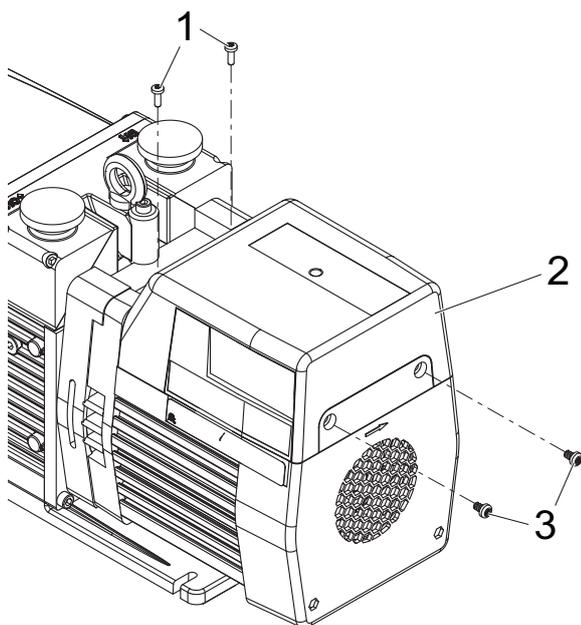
Obere Motorabdeckung entfernen/anbringen
